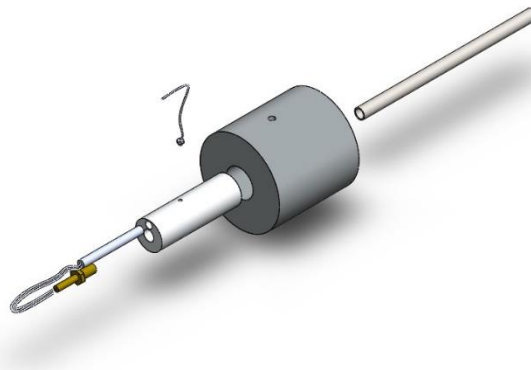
Vista explosionada cabezal de extrusión. Fuente: Propia.
